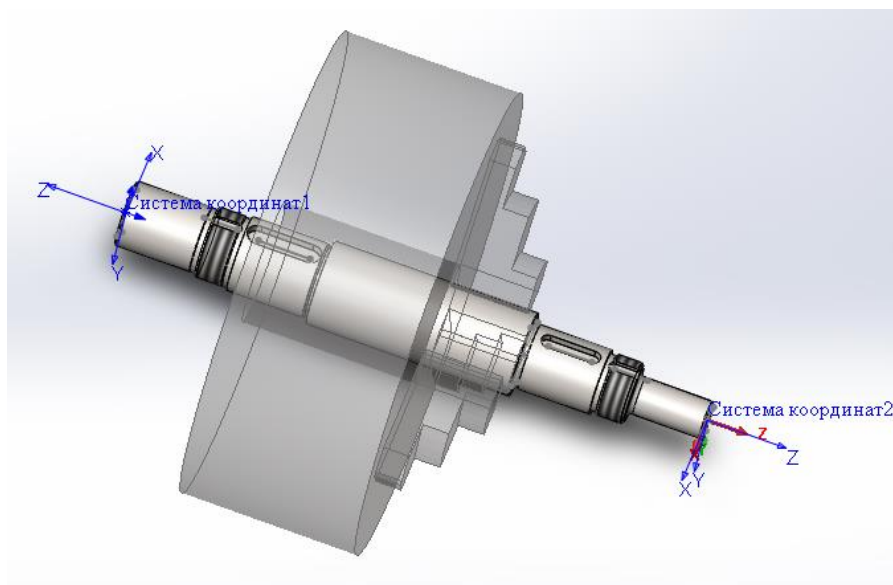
закріплення деталі «Вал» на токарному верстаті.
